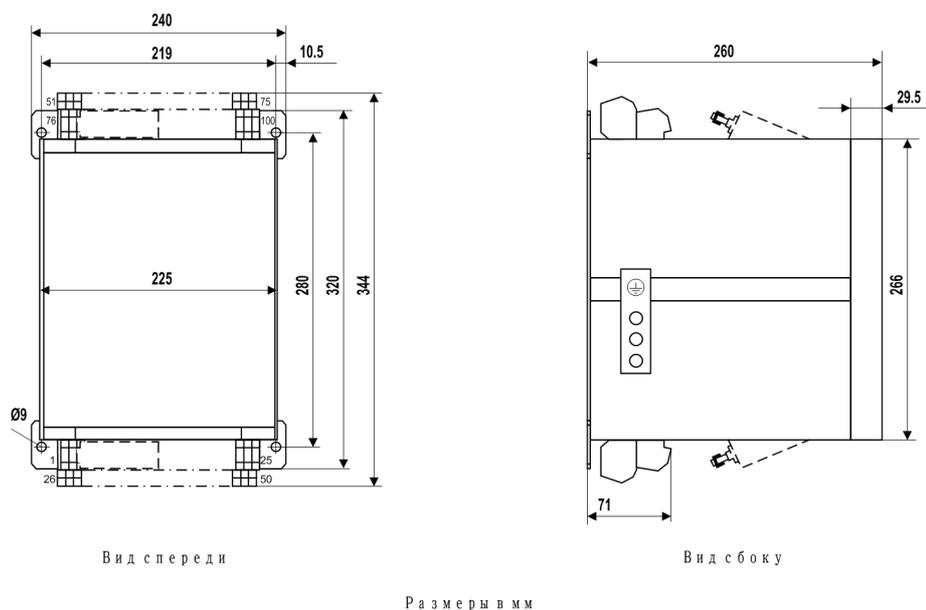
Размерный чертеж устройства 7SJ64 для поверхностного монтажа на панели (размер корпуса 1/2)
